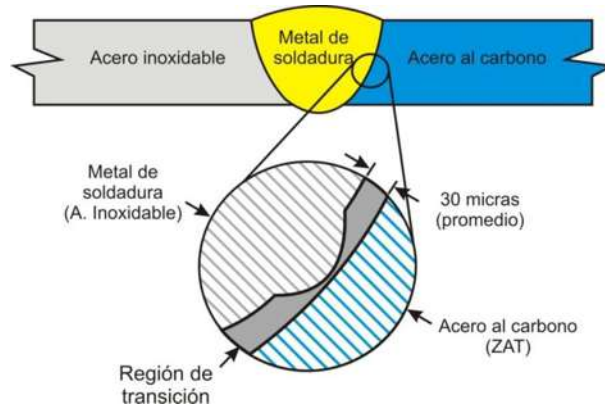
6.- Región de transición en las uniones soldadas disímiles.
